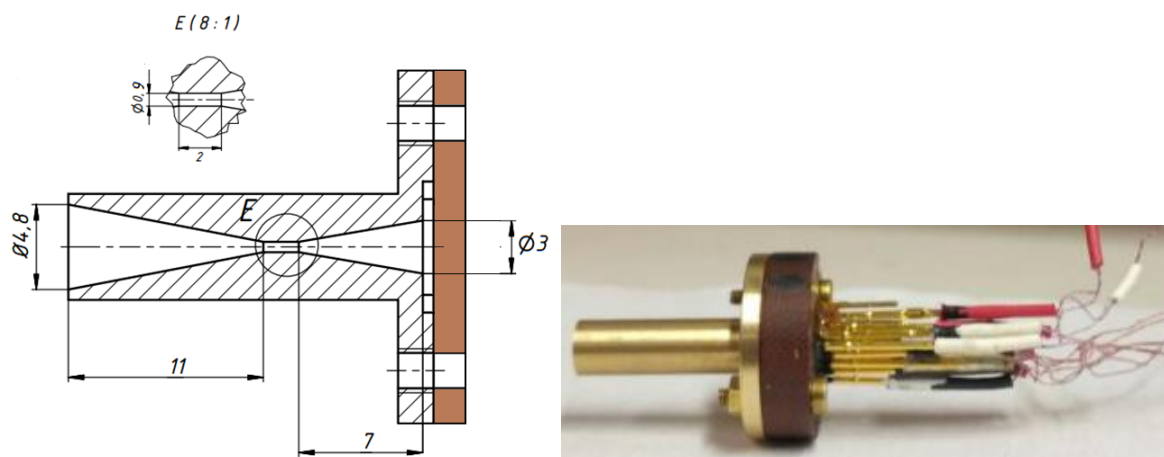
Чертеж и изготовленное согласующее устройство: приемный конический рупор длиной 11 мм, круглый волновод длиной 2 мм и диаметром 0,9 мм и выходной конический рупор длиной 7 мм
